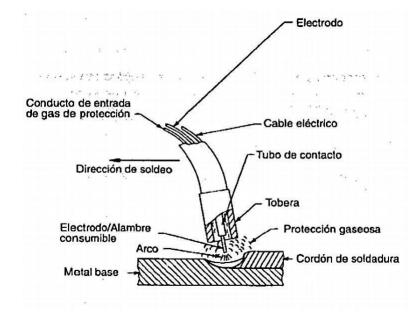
Esquema del proceso de soldadura GMAW
